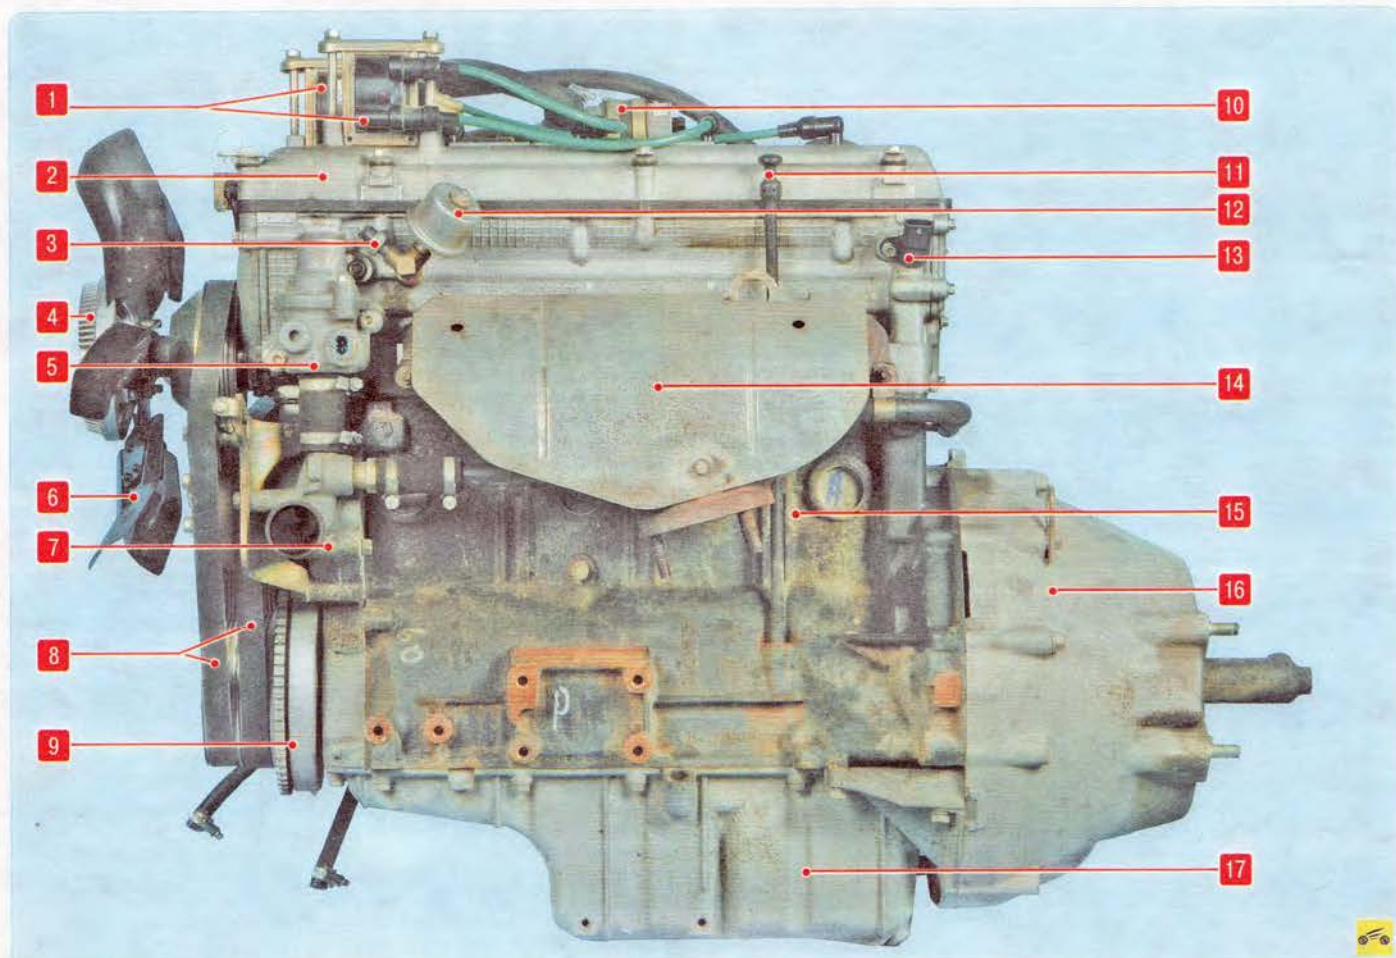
Двигатель ЗМЗ-409 (вид слева): 1 – катушки зажигания; 2 – крышка головки блока цилиндров; 3 – датчик аварийного падения давления масла; 4 – вязкостная муфта; 5 – корпус термостата; 6 – вентилятор; 7 – водяной насос; 8 – ремни привода вспомогательных агрегатов; 9 – шкив коленчатого вала; 10 – регулятор холостого хода; 11 – указатель (щуп) уровня масла; 12 – датчик указателя давления масла; 13 – датчик положения распределительного вала; 14 – термозан выпускного коллектора; 15 – блок цилиндров; 16 – картер сцепления; 17 – масляный картер
